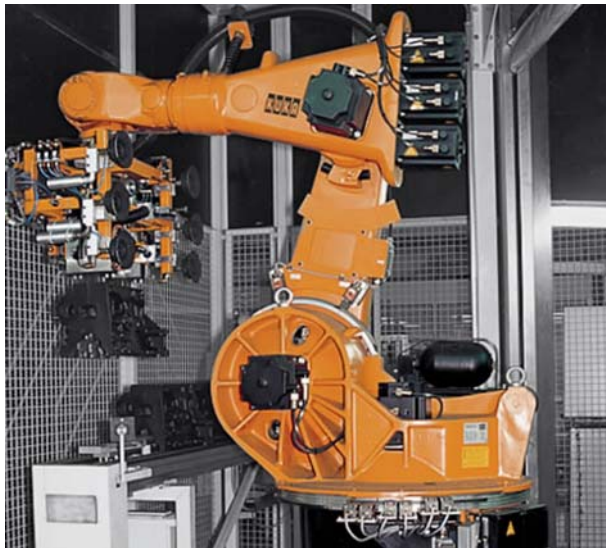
Манипуляции с блоками цилиндров двигателей
